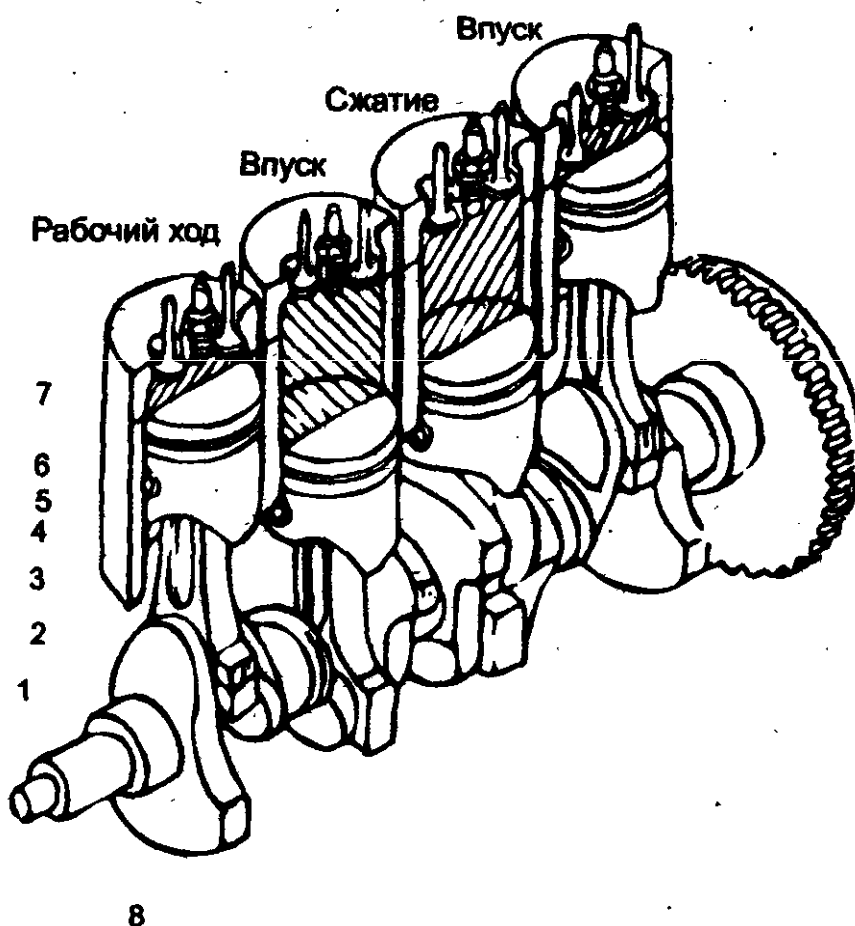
Порядок работы четырехцилиндрового двигателя:
